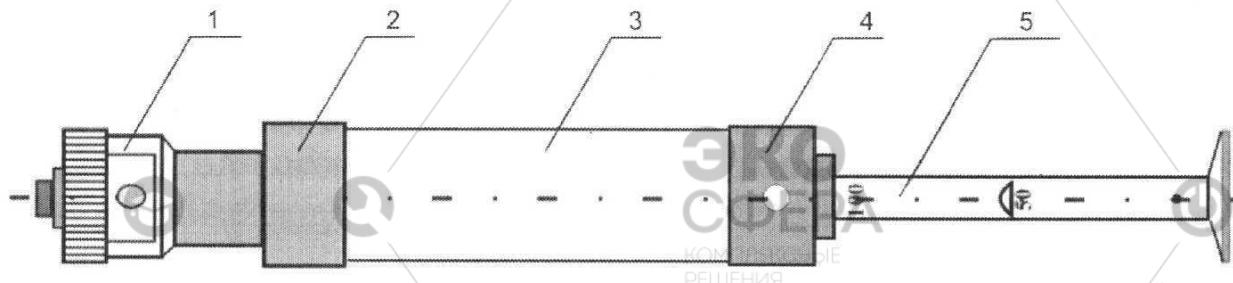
Внешний вид насоса-пробоотборника ручного НП-3М:
